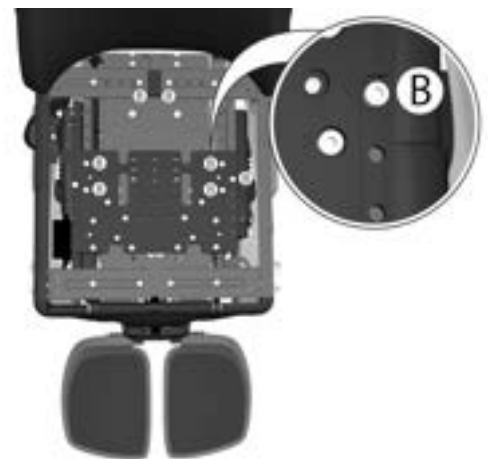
Die Position des hinteren Sitzrahmenabschnitts (Rückenlehnenposition) ist mit fünf Schrauben festgelegt. Sie sind mit dem Buchstaben B markiert.
